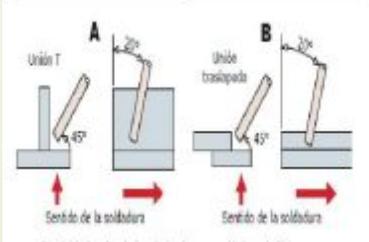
Angulos de los electrodos para soldadura de filete
